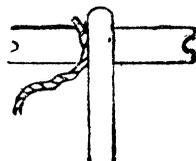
Разрез вала в колесе, закрепленного шнурком.
